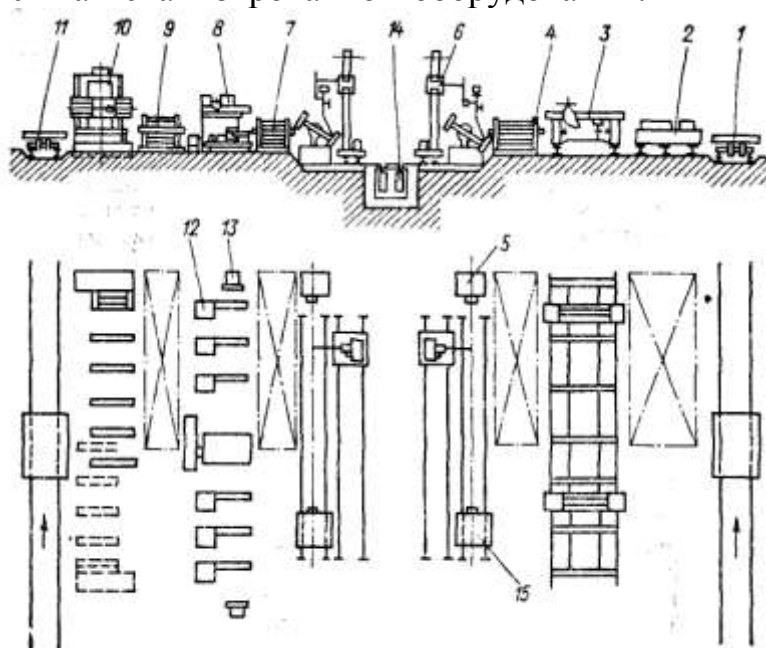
Схема поточной линии изготовления сварных двутавровых балок
